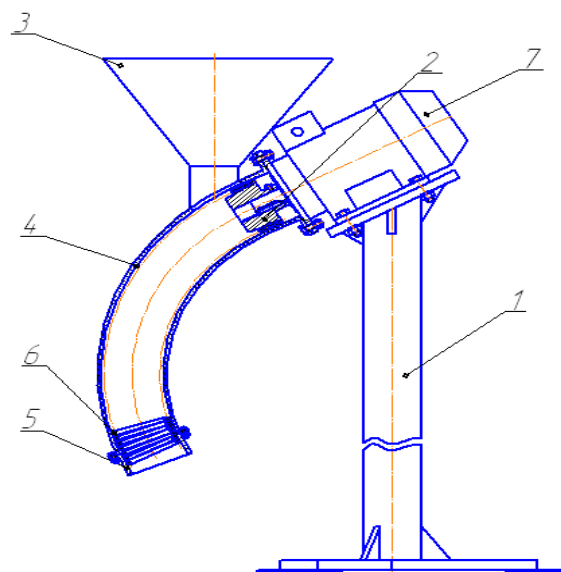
Активатор пружинный: 1 – стойка; 2 – насадка; 3 – загрузочный бункер; 4 – корпус; 5 – опора; 6 – пружина; 7 – электродвигатель
